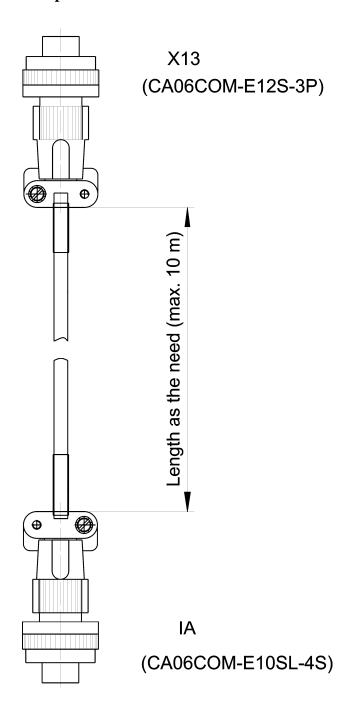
Impulsaufnehmerkabel mit Stecker
